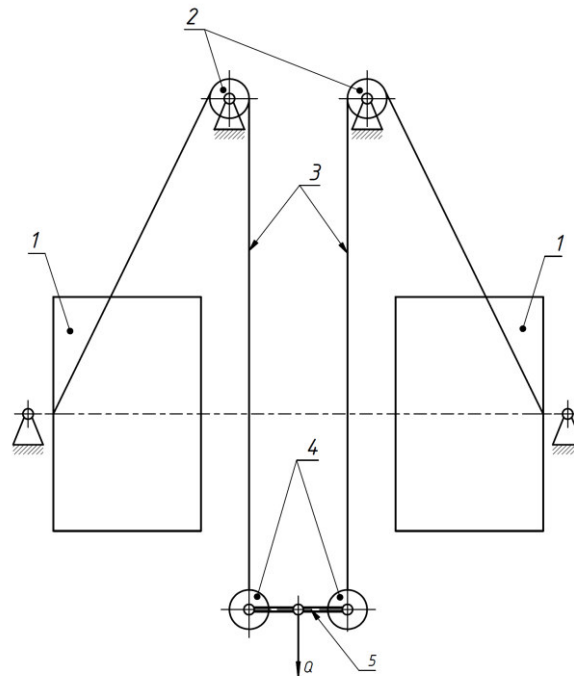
Схема запасовки каната привода подъема телекамеры: 1 – барабан; 2 – блок; 3 – канат; 4 – коуш; 5 – балансир [The wire rope of the mast lifting drive: 1 - drum; 2 - block; 3 - rope; 4 - shackle; 5 - balancer]
